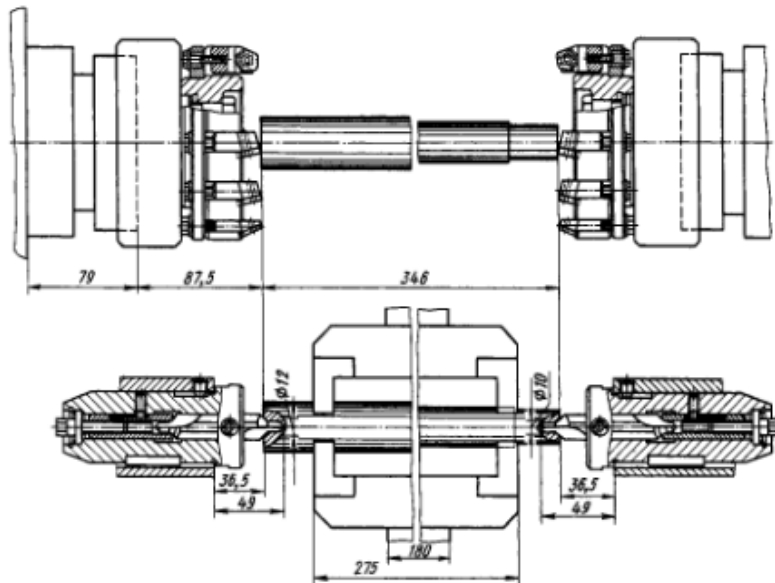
Налаштування фрезерно-центрувального верстата
